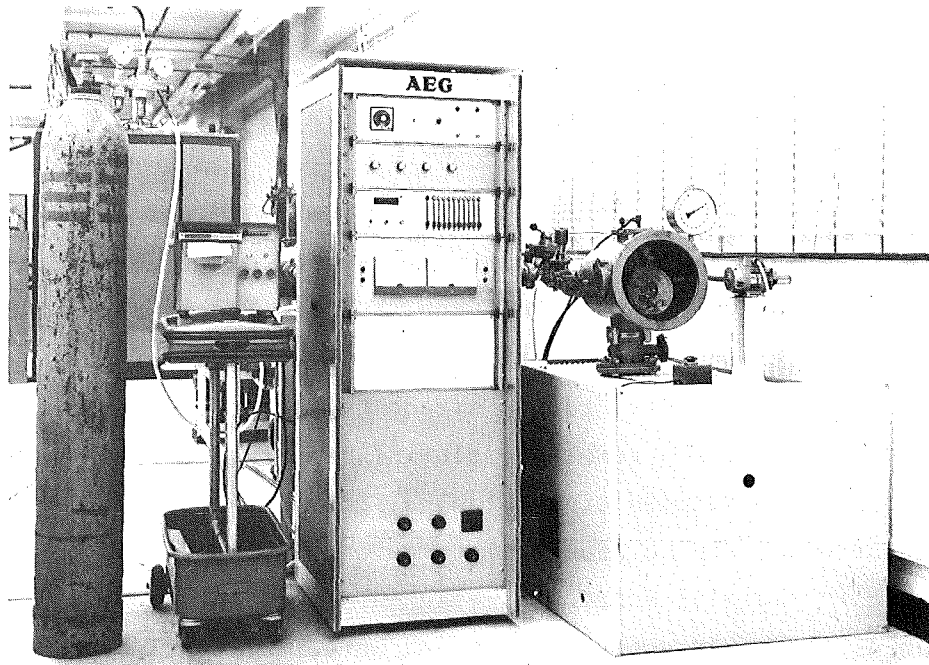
Rohrschweißkopf Versuchsaufbau
